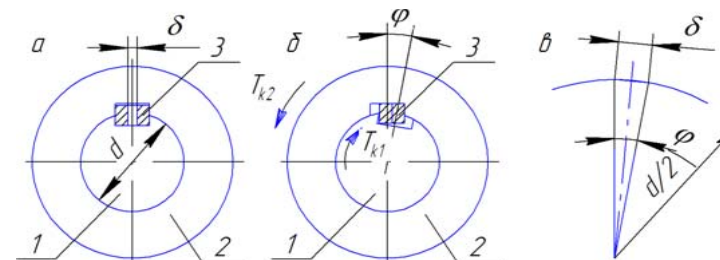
Схеми роботи з'єднання типу "вал-маточина" з пружною призматичною шпонкою:
